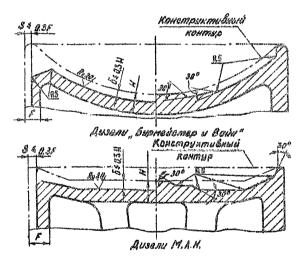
Подготовка деница и наружной цалиндрической поверхности головка поршня к восстановлению
